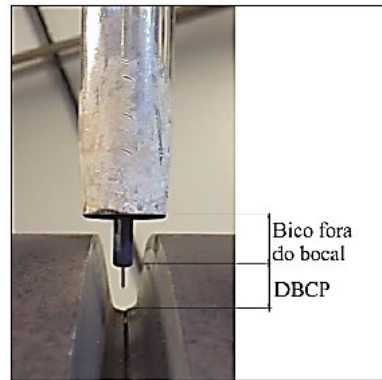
Bocal e bico de contato adaptados para a soldagem do passe de raiz automatizado. Fonte: [22]
